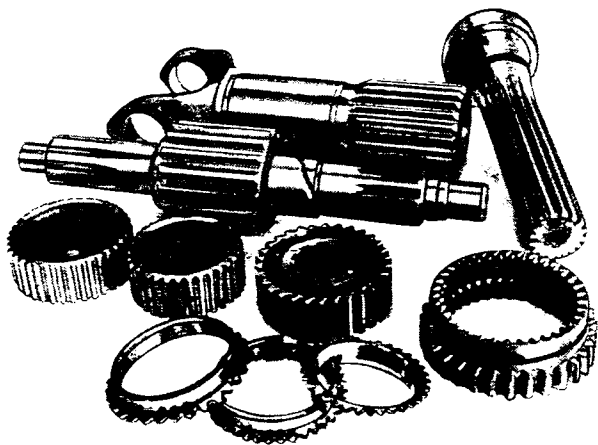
Типы деталей, обрабатываемых твердосплавными червячными фрезами сборной конструкции
